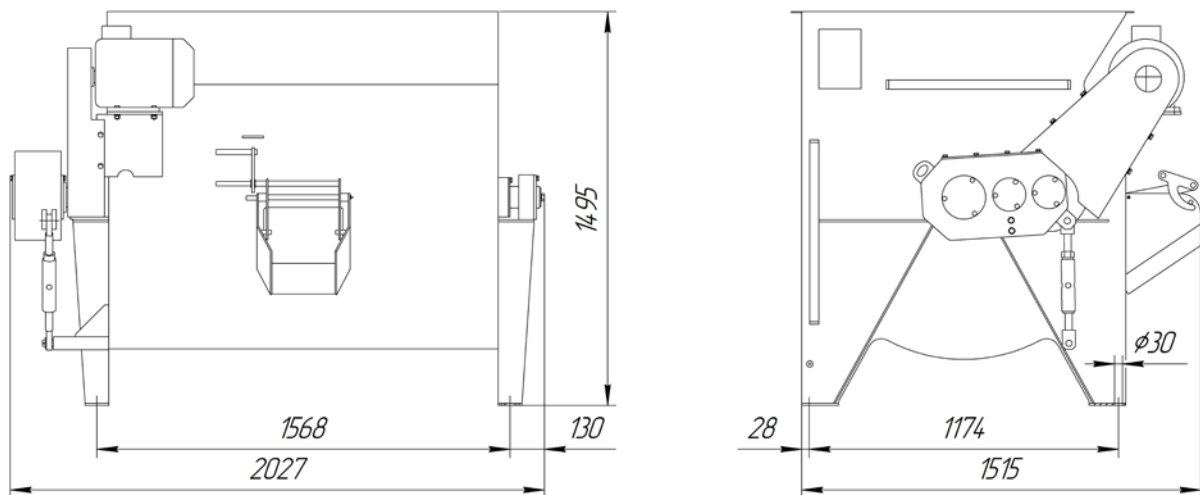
Габаритно-присоединительные размеры СГ-1000-А.
